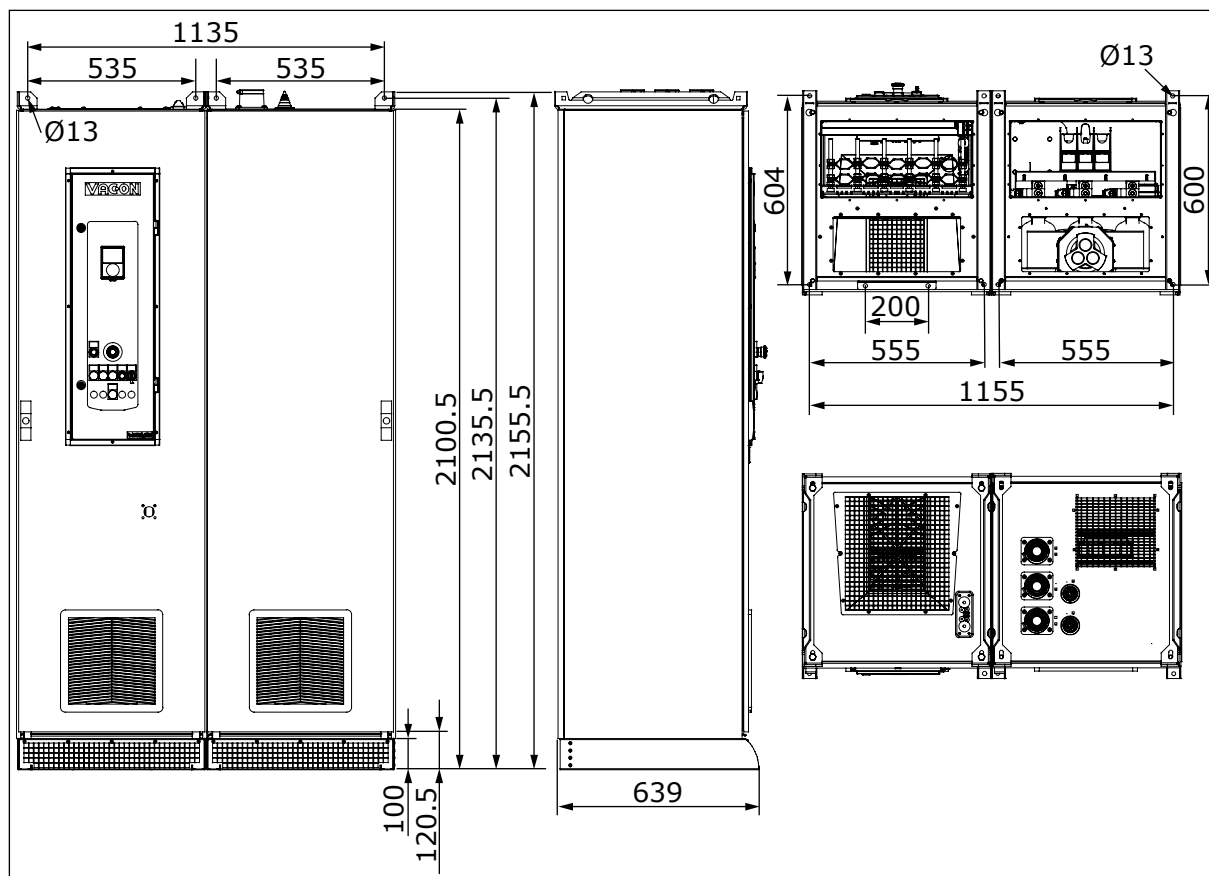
Mått på skåp med tillvalet sinusfilter, MR10, [mm], IEC
